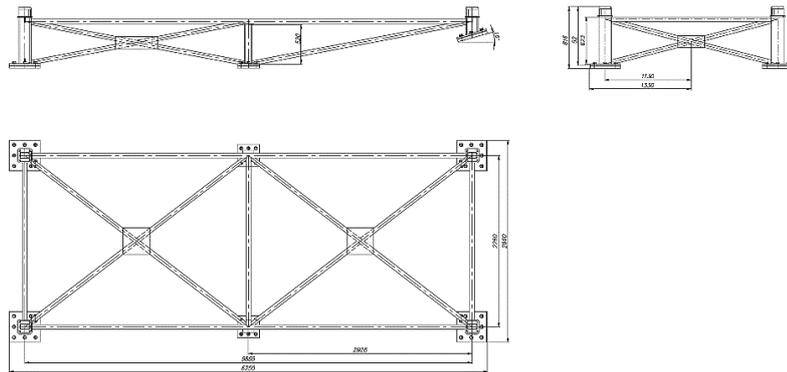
Чертёж рамы под рефрижераторный контейнер
